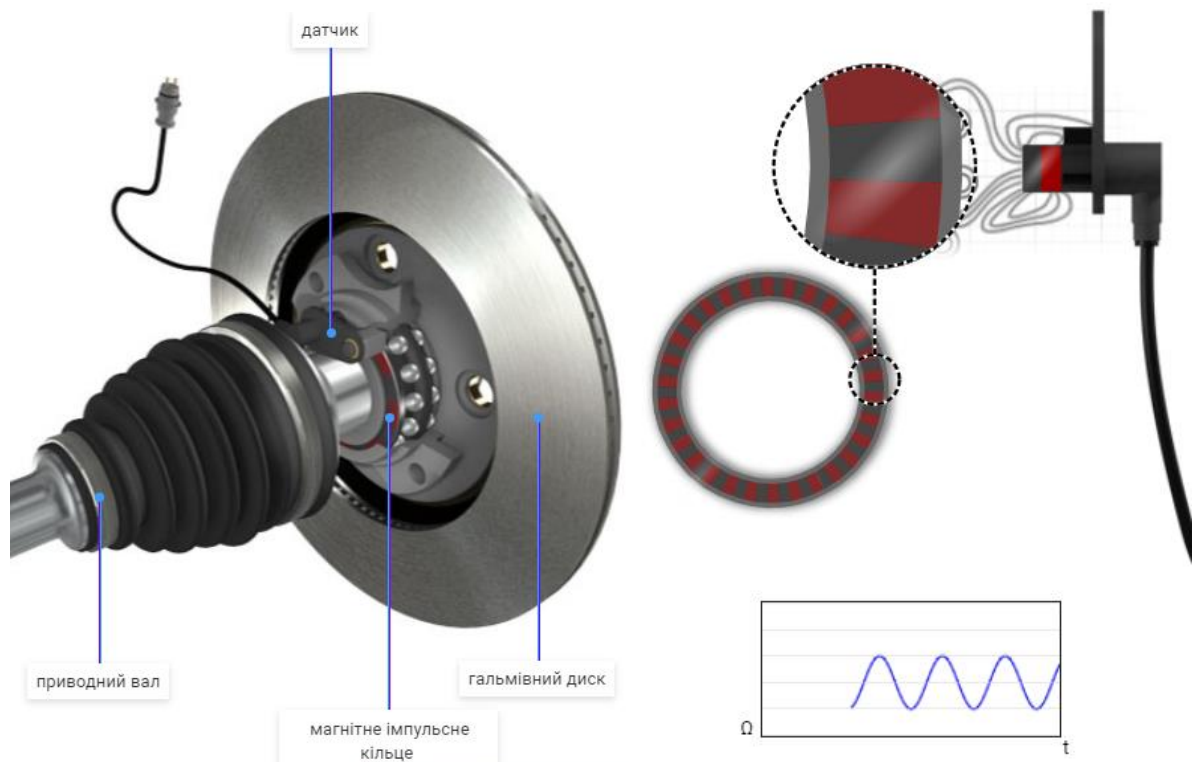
Магніторезистивний давач обертів колеса
